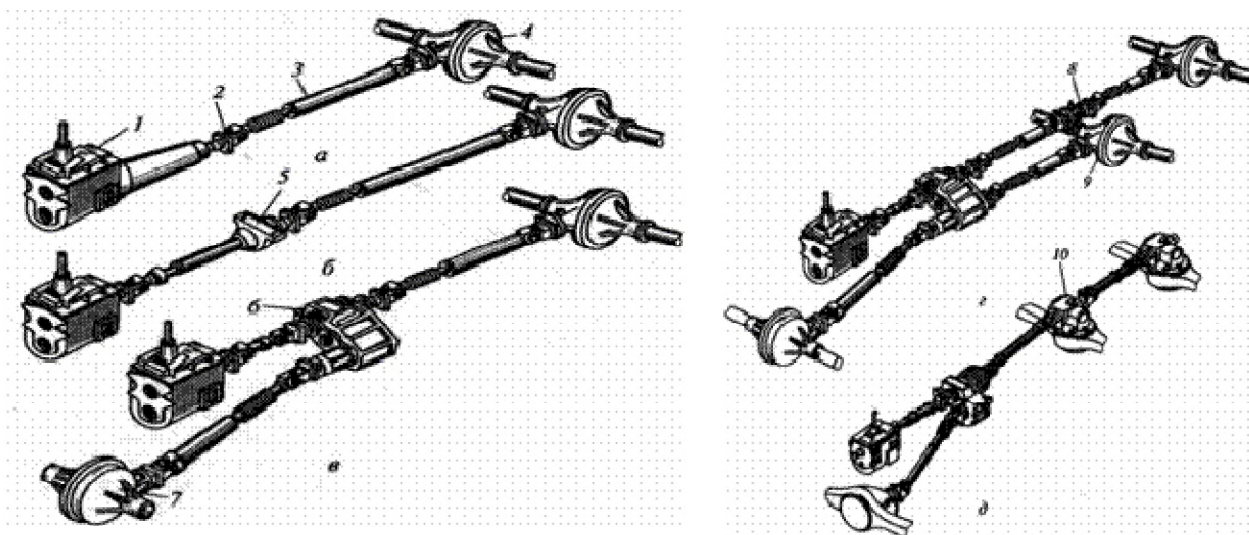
Карданные передачи для автомобилей с различной колесной формулой
